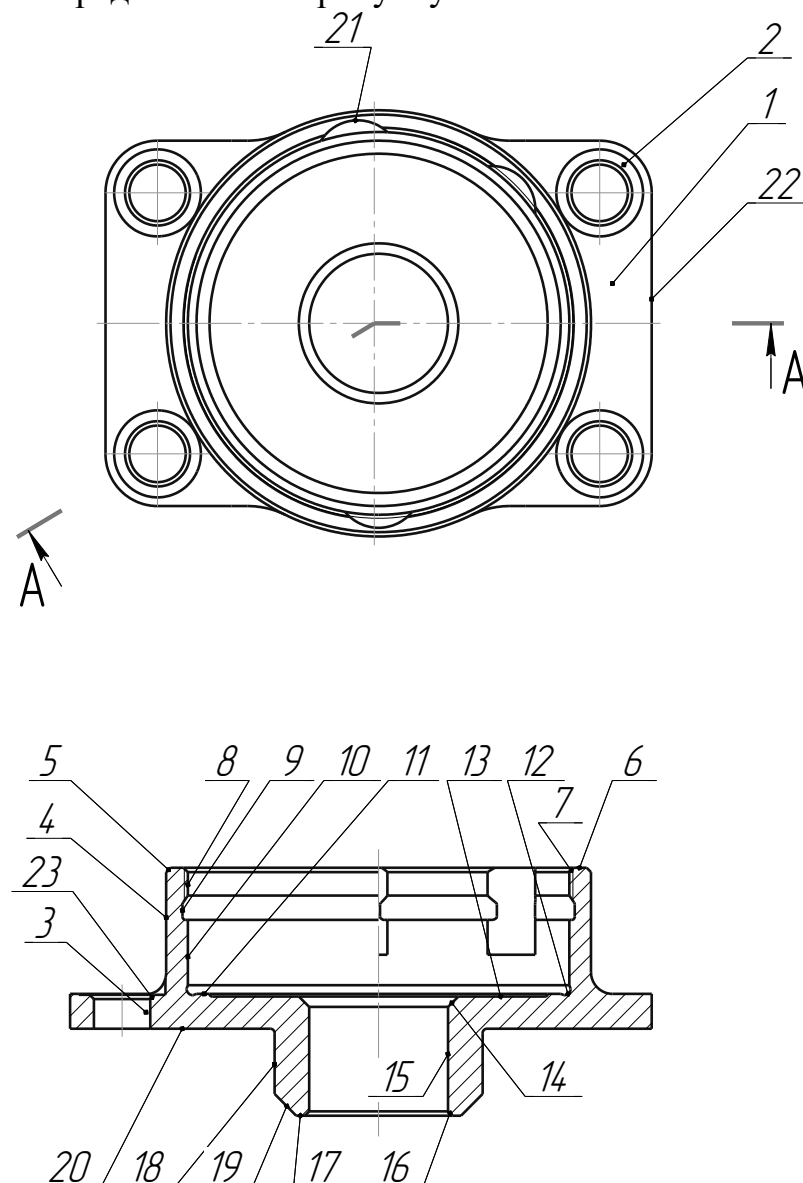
Ескіз деталі корпус із позначенням поверхонь
